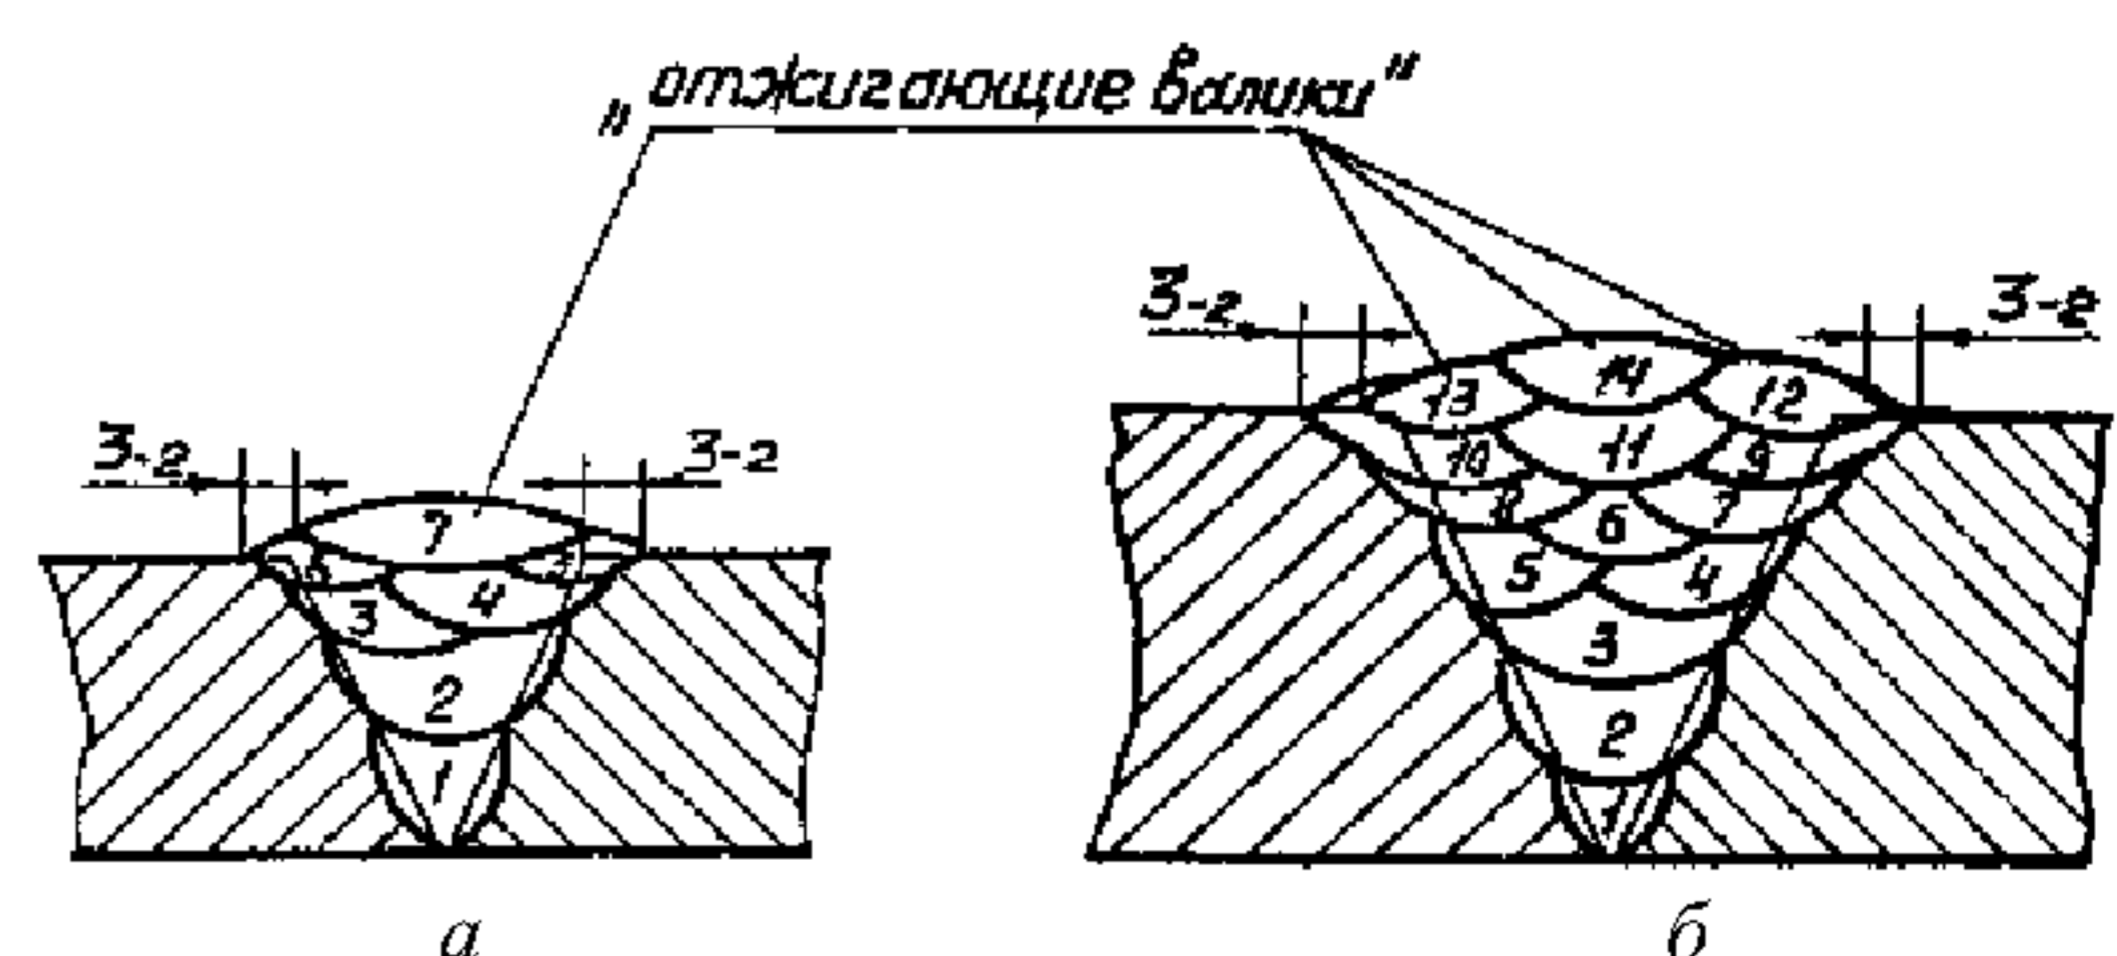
Порядок наложения валиков при многопроходной сварке стыковых соединений по методу «отжигающего валика»:
